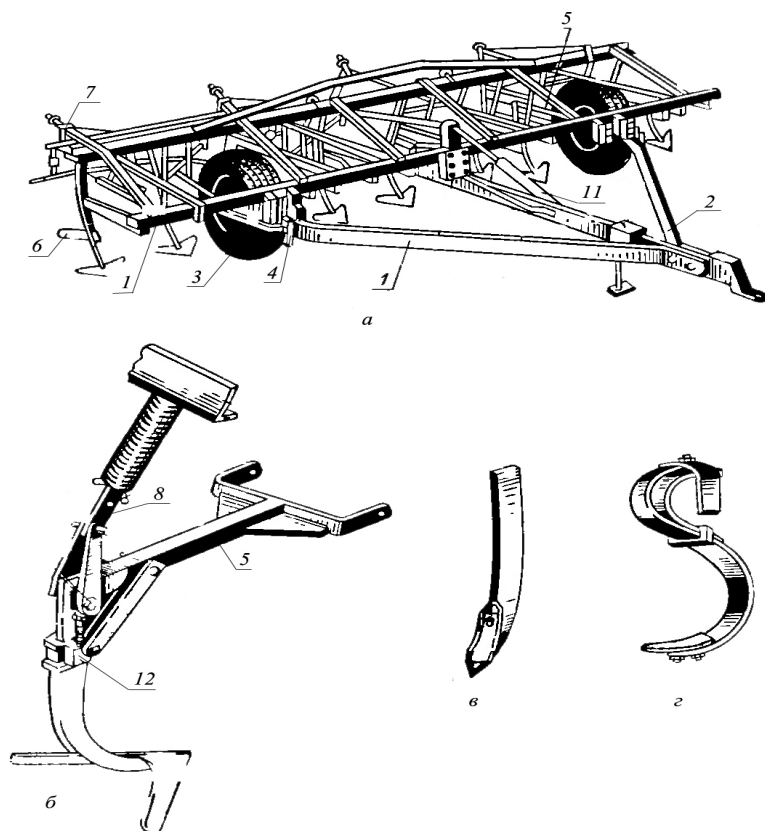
Прицепной культиватор КПС-4а – общий вид; б – стрелчатая лапа; в и г – рыхлительные лапы.
